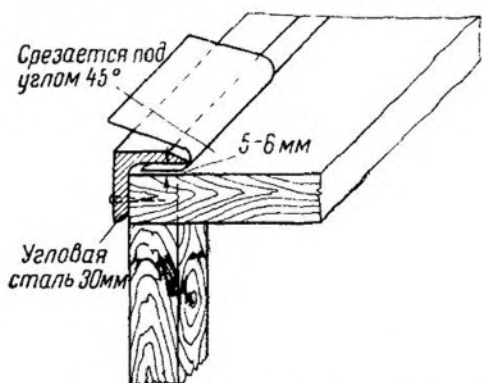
Приспособление к верстаку конструкции Л. А. Ланшова
